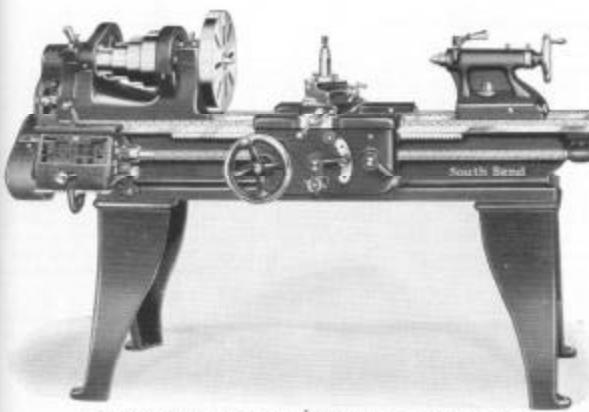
Torno inglês com engrenagens de mudança rápida.
